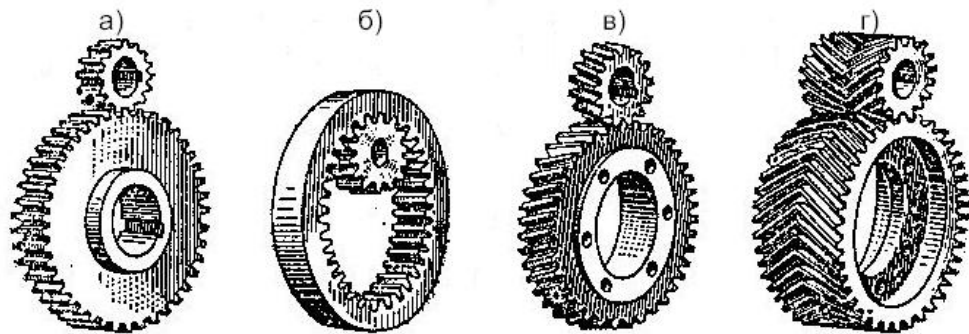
Зубчаті циліндричні колеса та зачеплення з паралельними осями;
